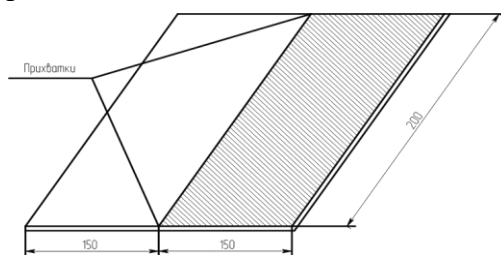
Схема сборки пластин для выполнения лабораторной работы
